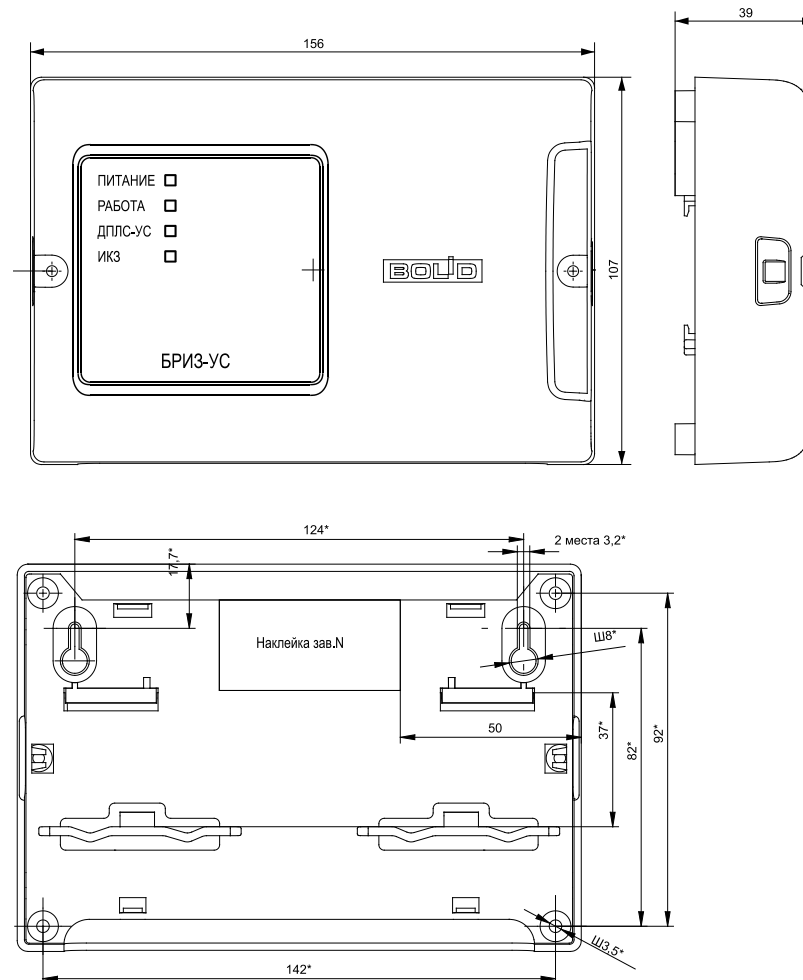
Габаритные и установочные размеры блока
